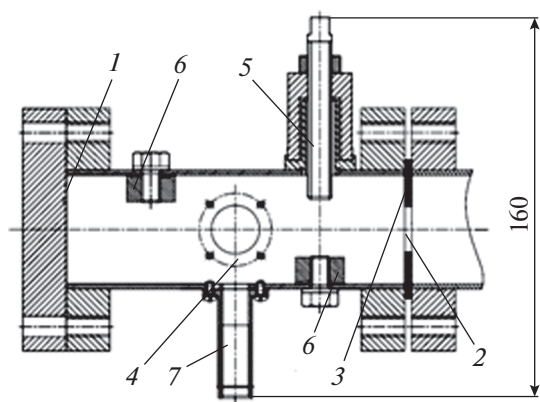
Вид с.в.ч.-резонатора в разрезе с вводом образца в область максимума магнитного поля. 1 — закорачивающая пластина; 2 — отверстия связи; 3 — индуктивная диафрагма связи; 4 — патрубки ввода образцов; 5 — настроечный штырь; 6 — настроечная бобышка; 7 — пирометр.
